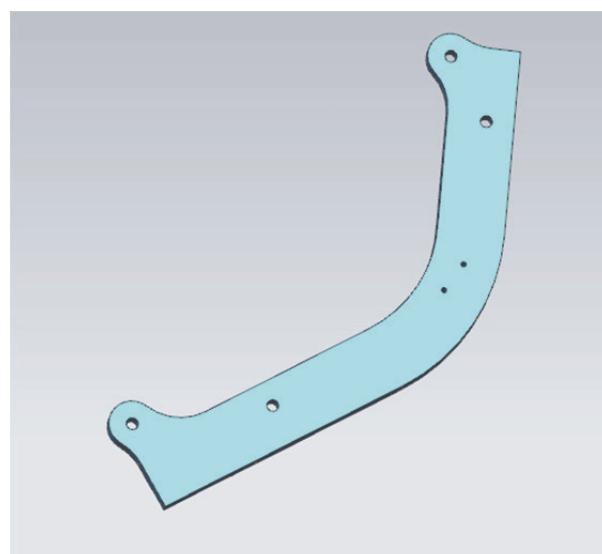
Модель исследуемого ложемента сборочного приспособления
